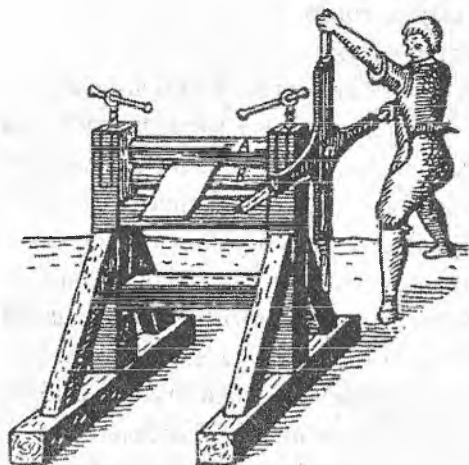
Прокатный стан дуо с цилиндрическими валками
